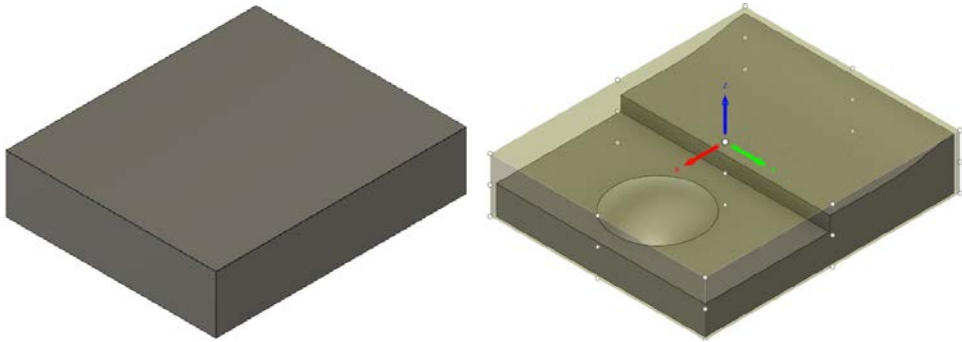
Barra de Toolox44 de dimensiones 100x60x60mm
